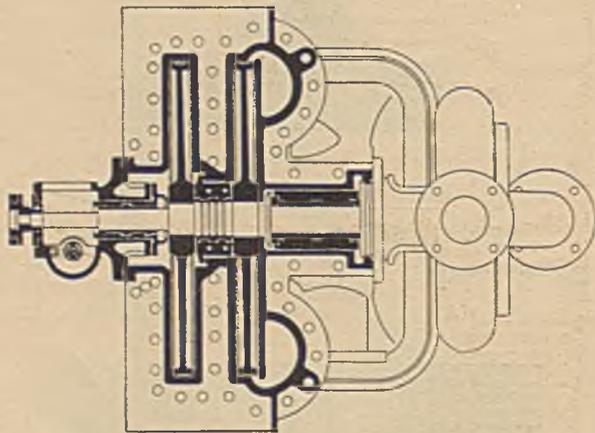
Querschnitt einer wagrechten Unionturbine.
